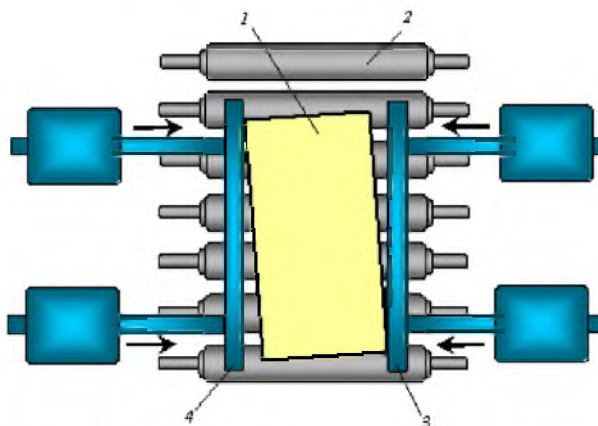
Манипулятор: 1 — прокатываемая полоса; 2 — рольганг; 3, 4 — линейки манипулятора
